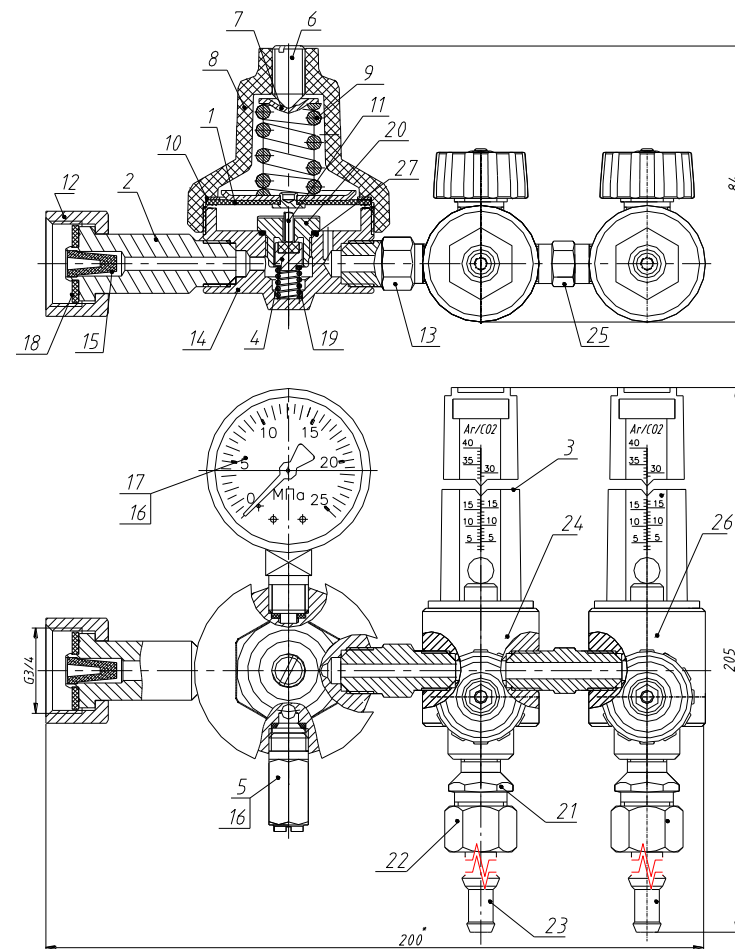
Регулятор расхода газа комбинированный (на два газа) с двумя ротаметрами крупногабаритный.
